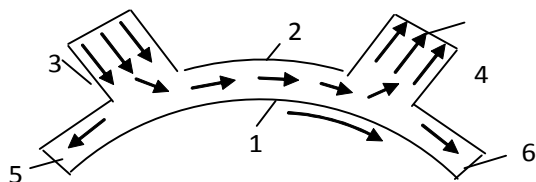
Схема устройства для сушки поверхности офсетного цилиндра:
